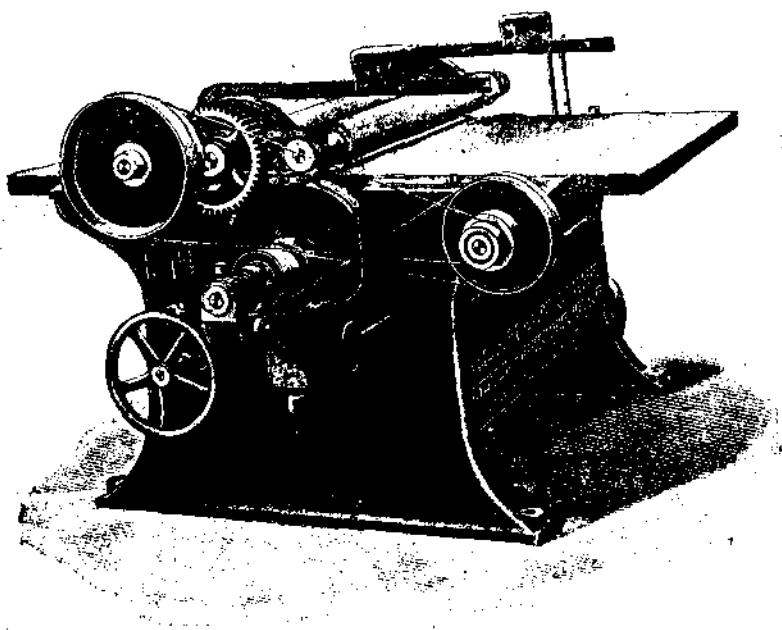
Шлифовальный станок с барабаном и автоматической подачей.
